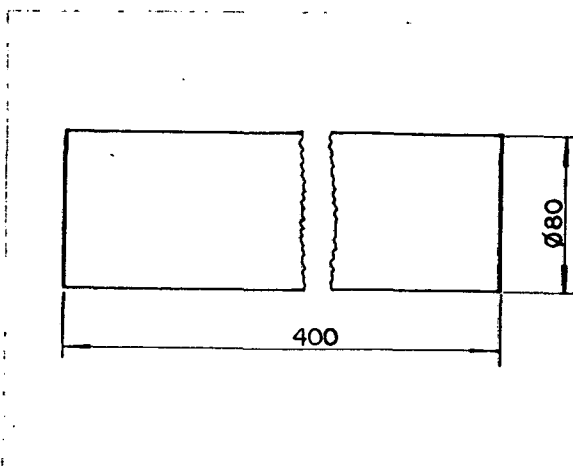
Dimensões do corpo de prova utilizado nos ensaios de torneamento e furação ortogonal.
